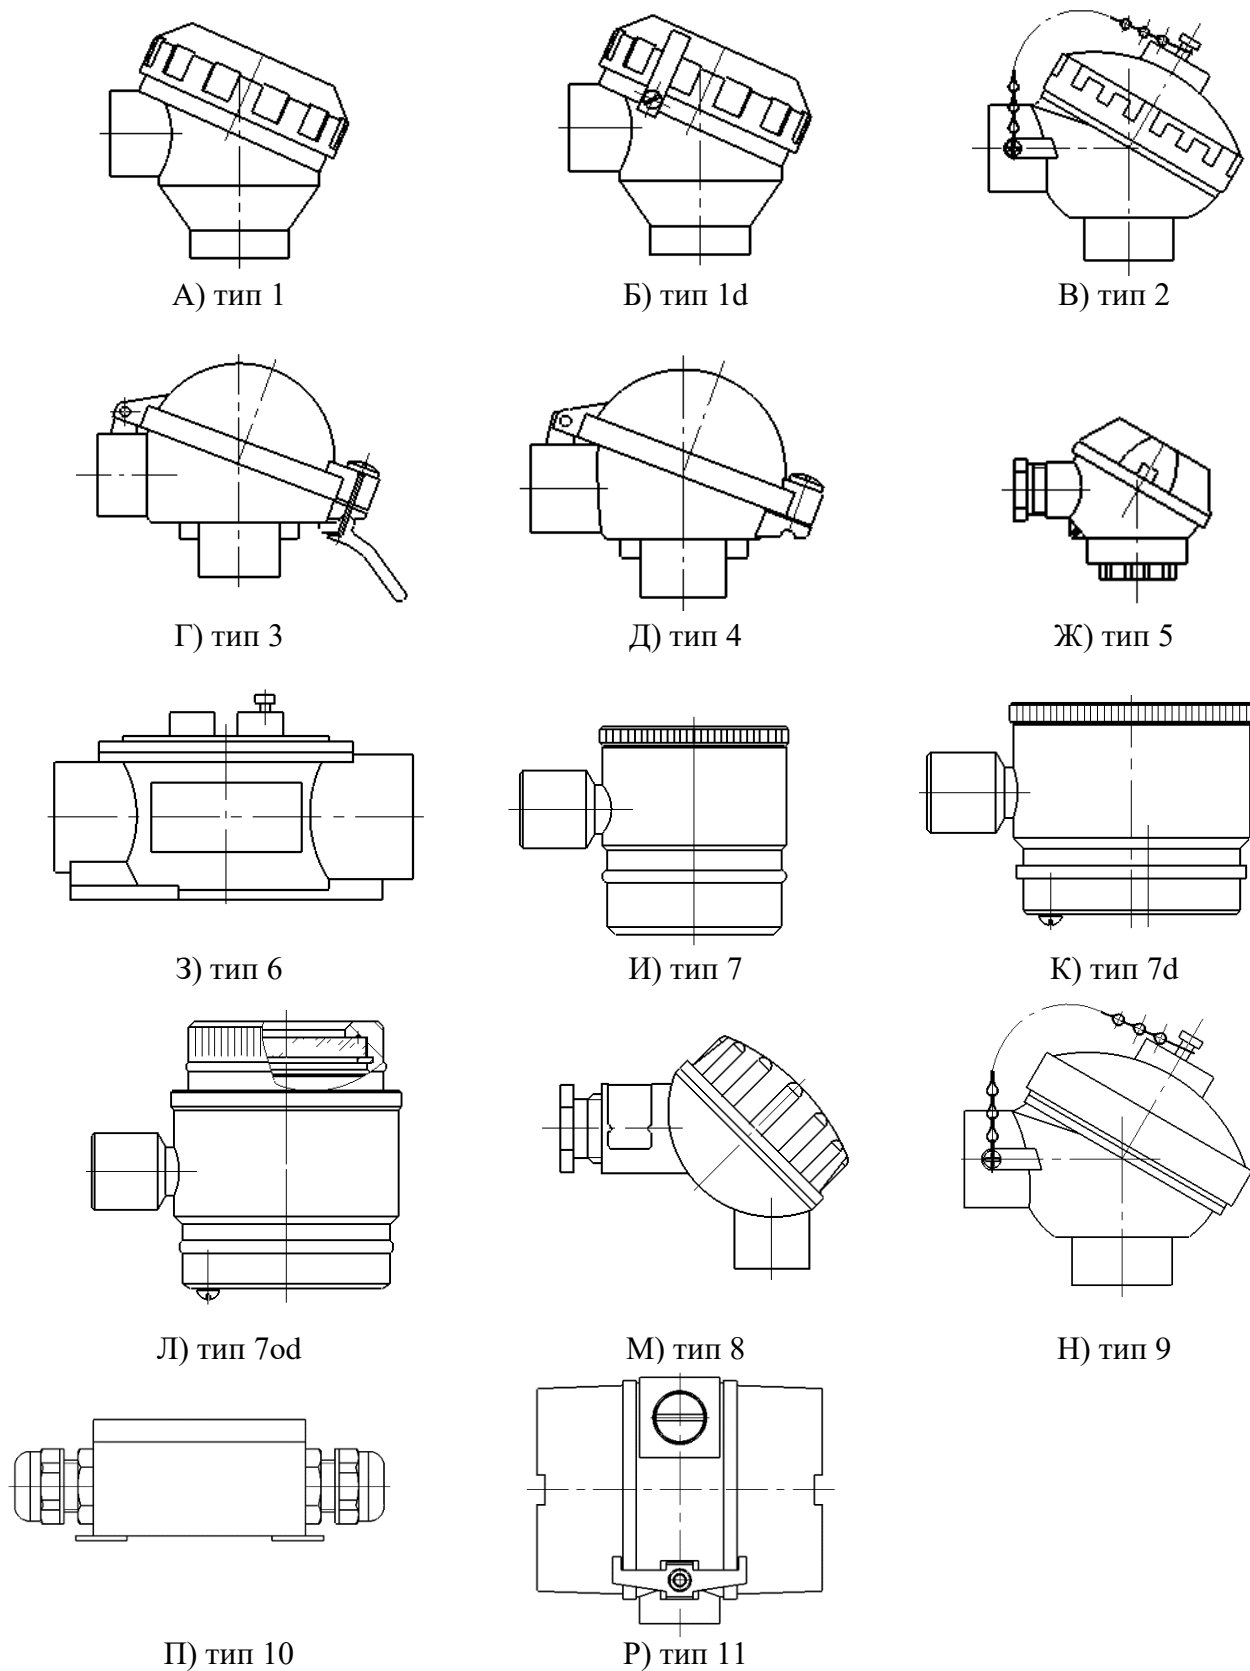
Общий вид конструктивного исполнения корпусов ТП
